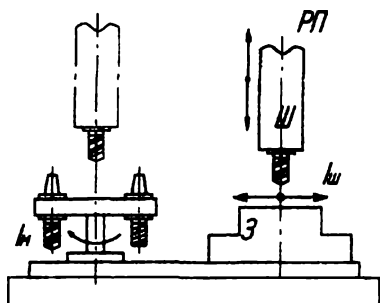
Схема автоматичної заміни інструмента за допомогою кінематики руху шпинделя і магазину
